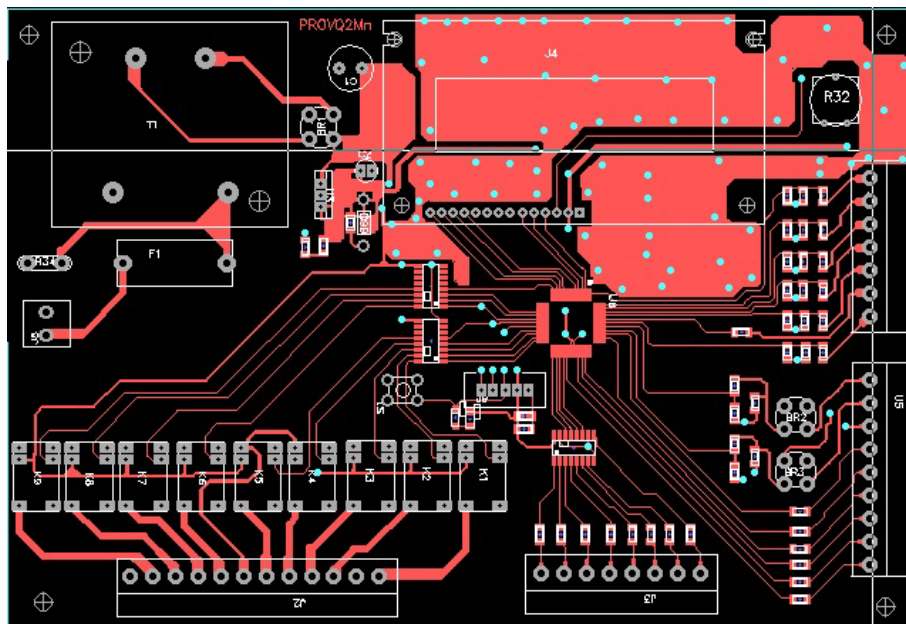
Impressió pantalla cara superior PCB (TOP)
